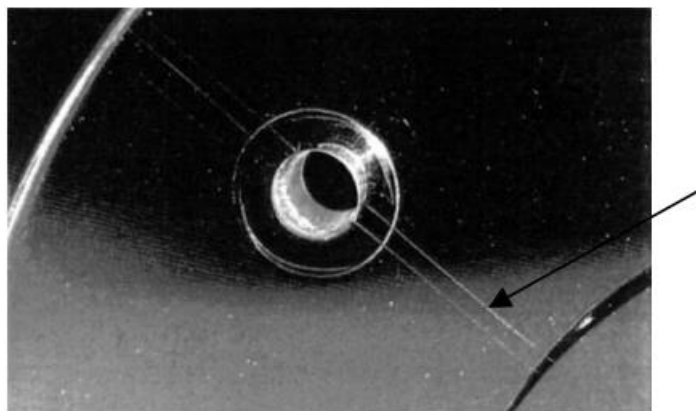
Linhas de soldadura causadas por efeitos geométricos [5]
